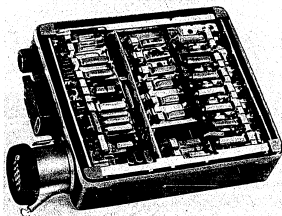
Innenchassis eines Funksprechgerätes mit Gummipuffern abgedeutert
